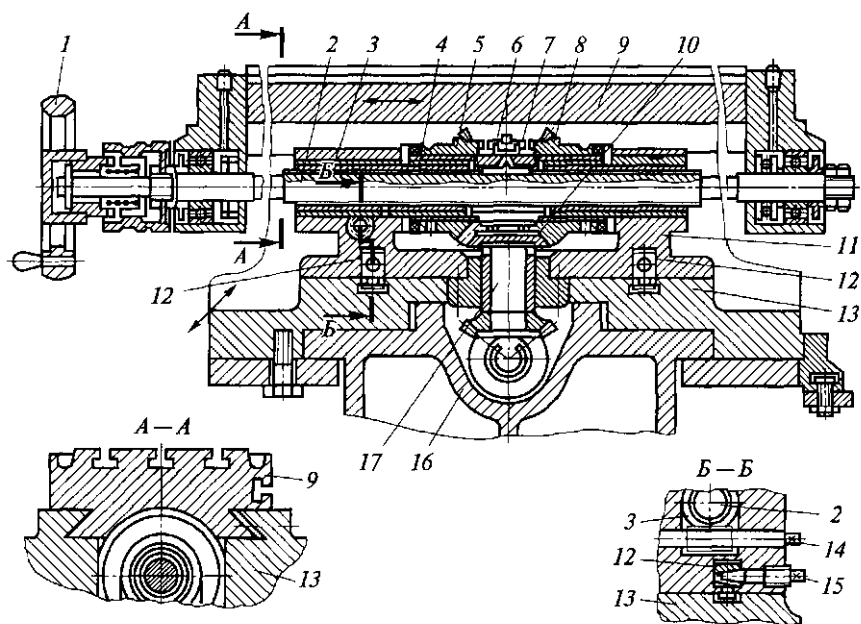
Стол и салазки горизонтального консольно-фрезерного станка:
